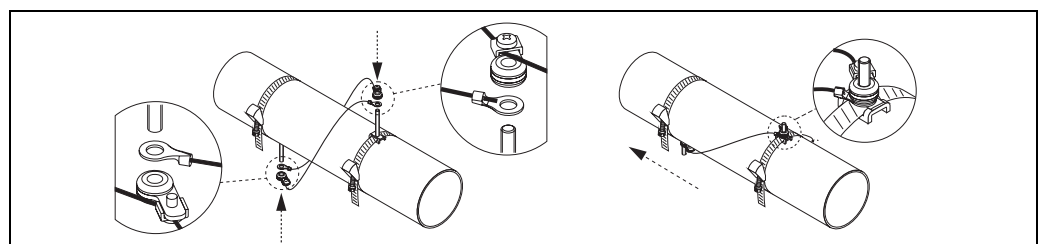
Posizionamento delle fascette di fissaggio (passaggi 2...4)
